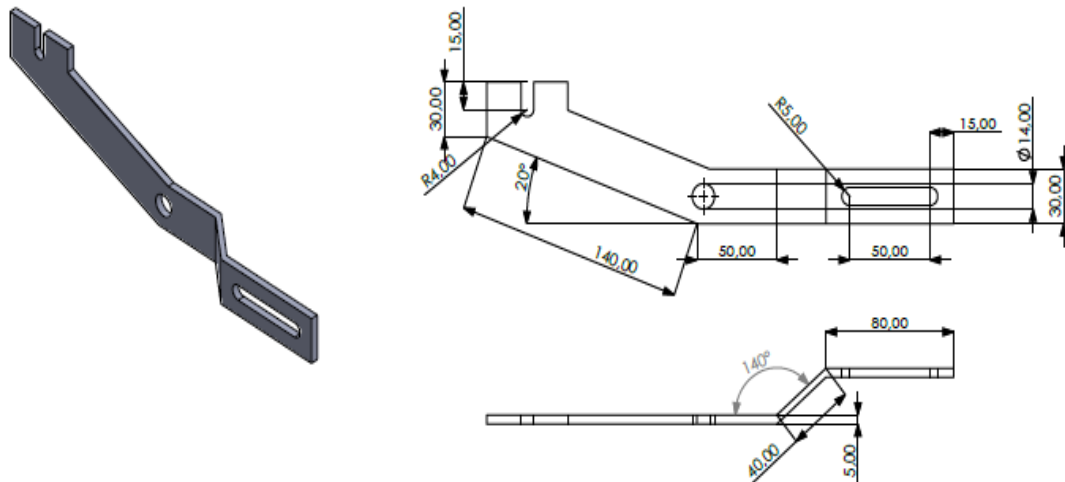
Vista alámbrica e isométrica de soporte derecho.
